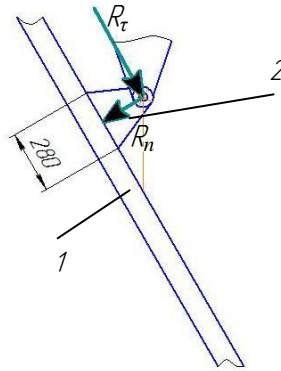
Схема для розрахунку зварного шва: 1 – вухо осі; 2 – рама
